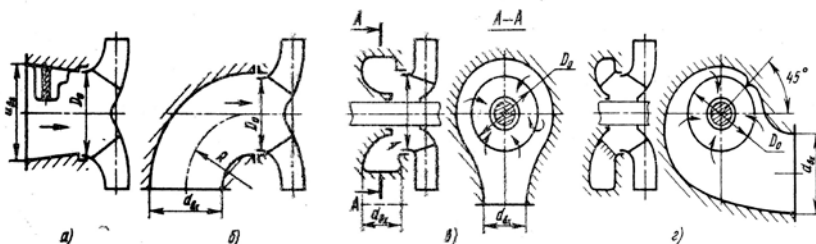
Схемы подводов центробежных насосов: а – конфузорный патрубок; б – изогнутое колено; в – кольцевая камера; г – полуспиральный подвод
